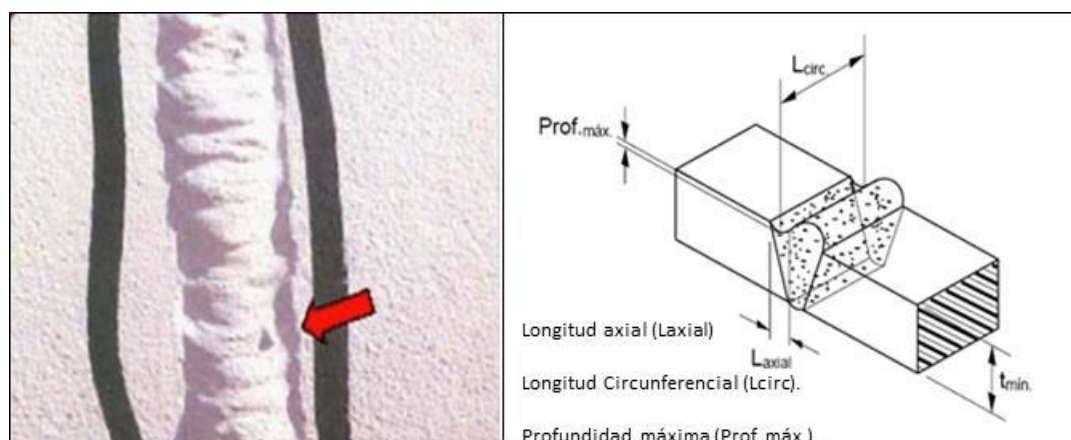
Comportamiento de un socavado en soldadura (7)
